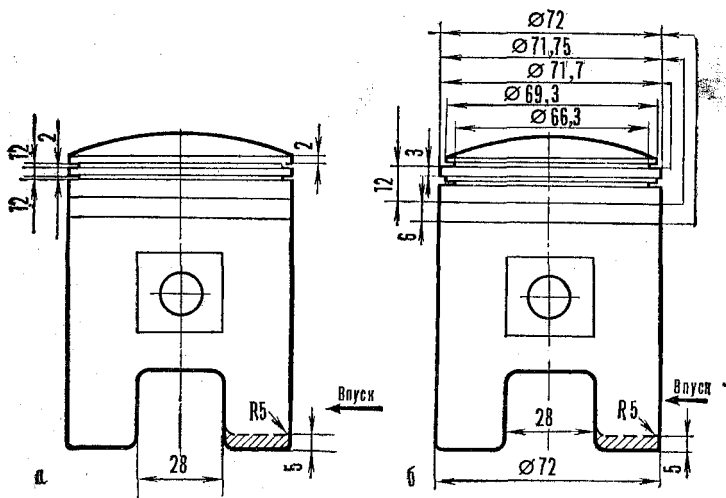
Поршни для форсированного двигателя ИЖ-11К: а — со стальными кольцами; б — с L-образными
